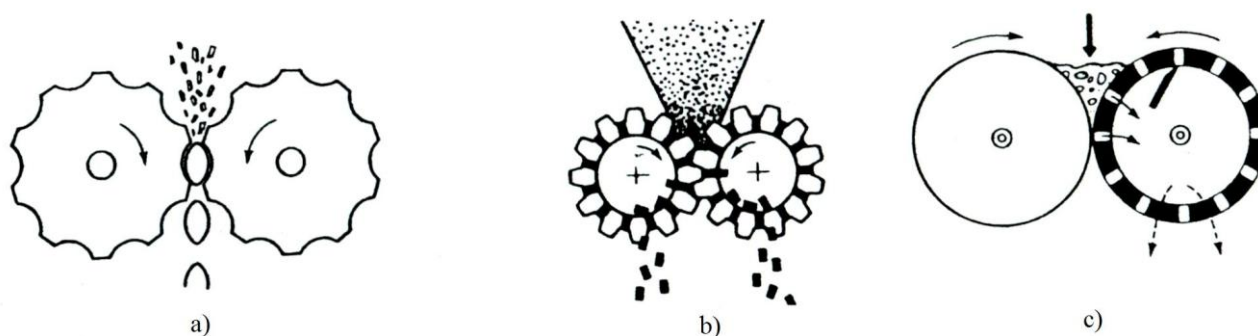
Equipo para compactado de briquettes y pellets; a) Compactador de briquettes por rodamiento; b) Equipo de compactación de pellets de engranaje; c) Extrusor de doble rodillo
